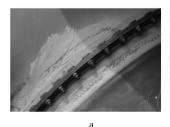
TB3 系列发动机的黑色高温漆失效 Fig. 6 Black anti-heat coating failure of TB3 turbo-shaft
